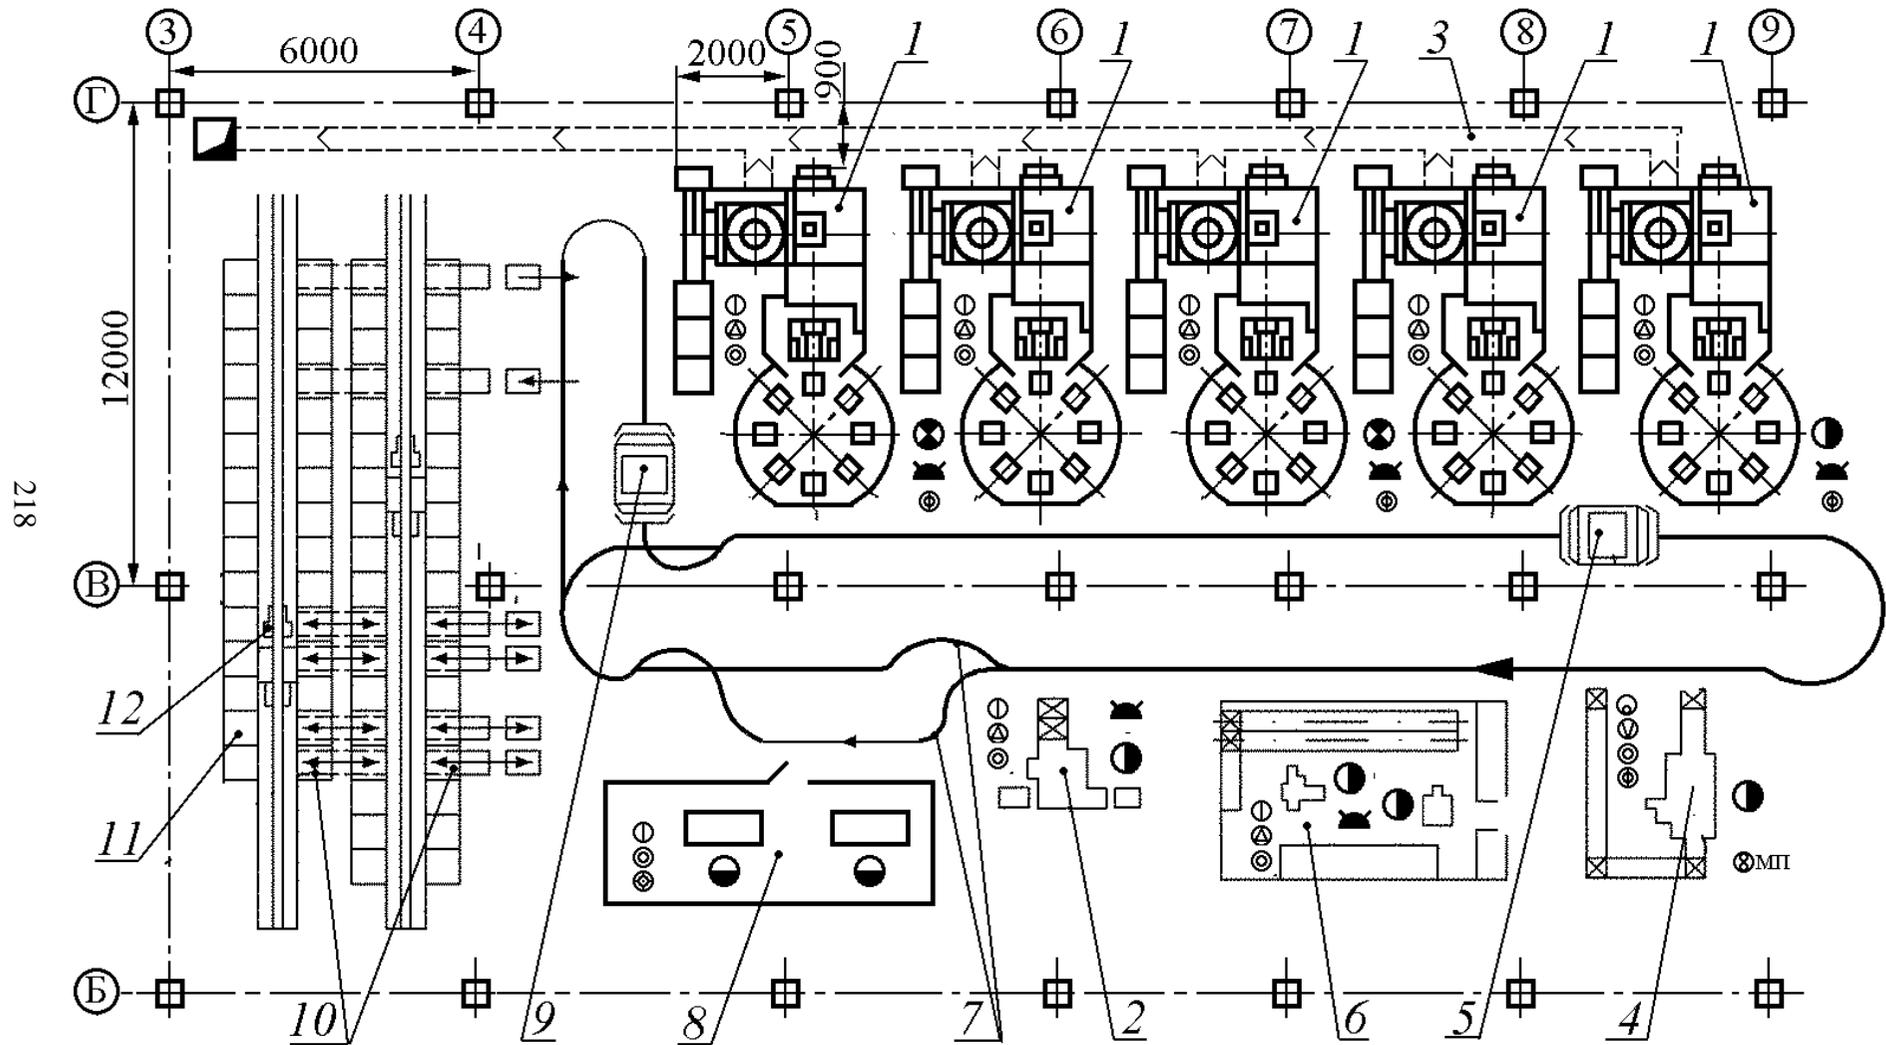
П14. ГПУ для обработки корпусных деталей:
